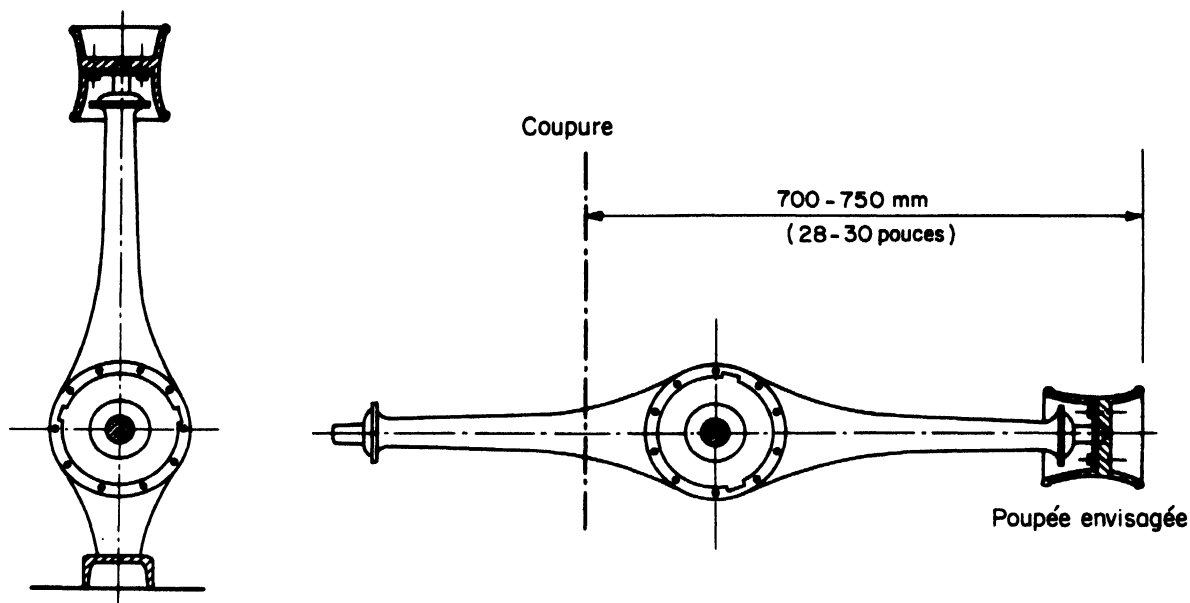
PLAN DE DECOUPAGE DU PONT-ARRIERE
